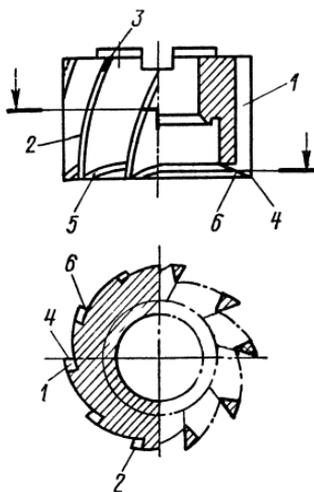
Геометрические элементы цилиндрической фрезы:
